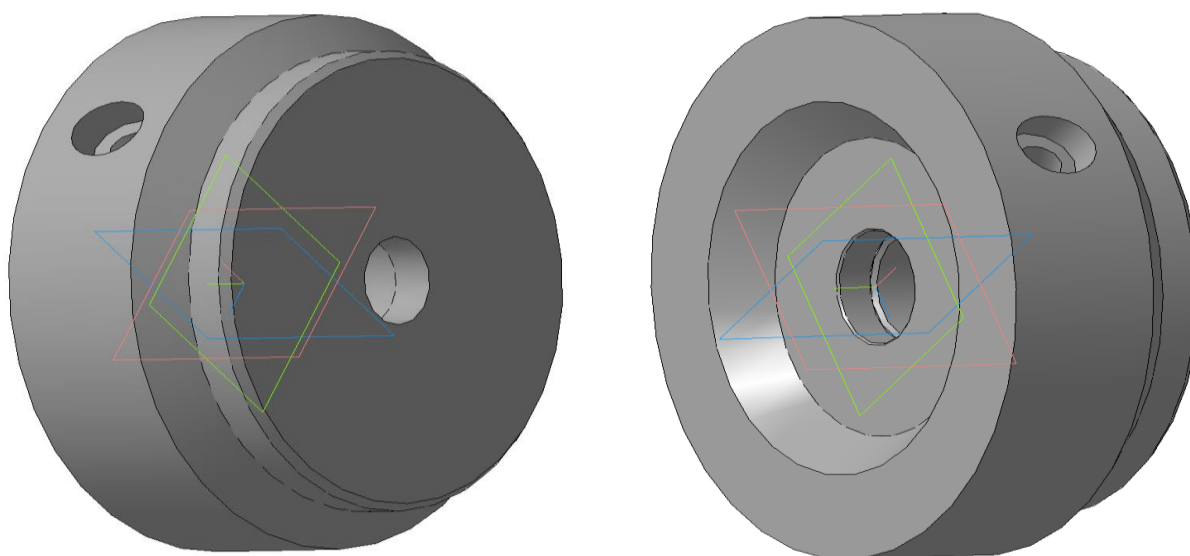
3D модель детали «Крышка цилиндра»
